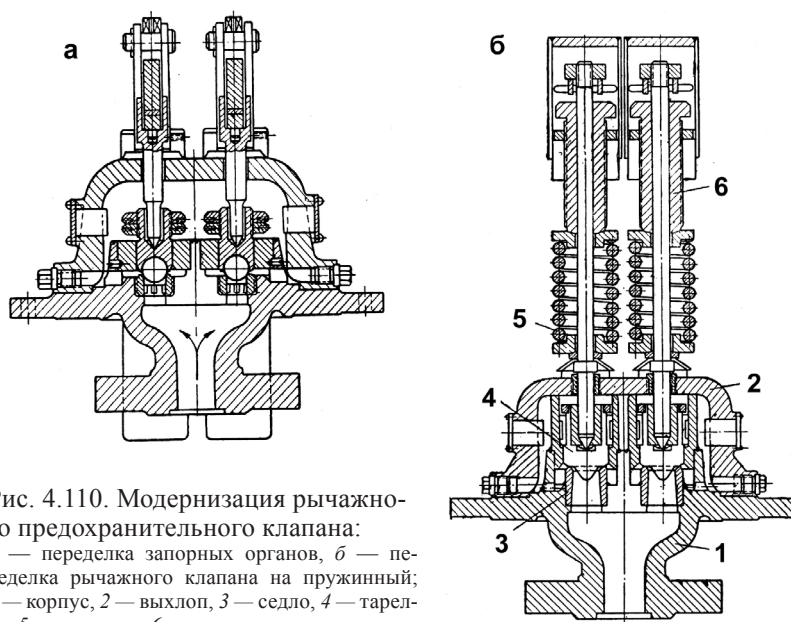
Модернизация рычажного предохранительного клапана: а — переделка запорных органов, б — переделка рычажного клапана на пружинный; 1 — корпус, 2 — выход, 3 — седло, 4 — тарелка, 5 — пружина, 6 — втулка
